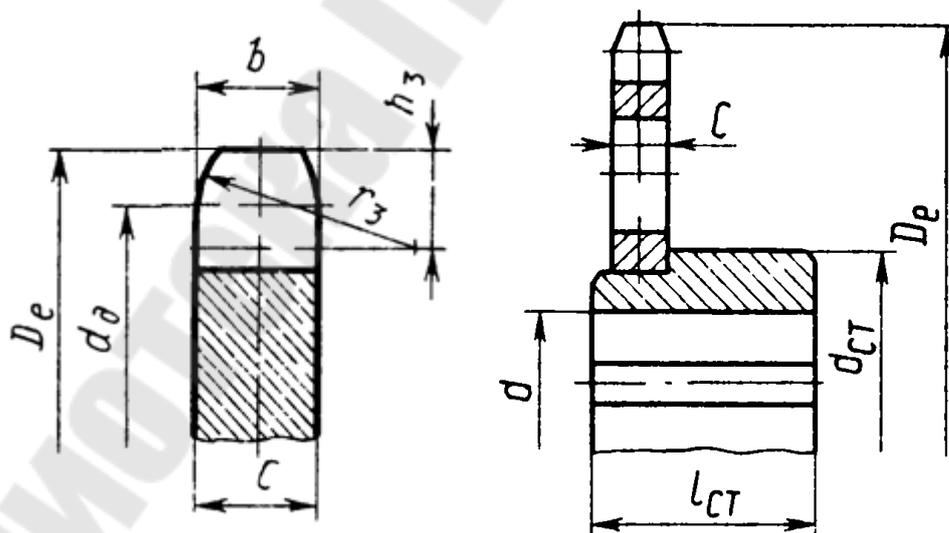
Конструкция звездочки втулочно-роликовых цепей с приварным ободом
